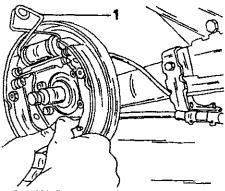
Вставить тормозные колодки сверху в колесный тормозной цилиндр и развести снизу, чтобы их можно было упереть в нижний упор. Пружинная скоба (1) препятствует выходу поршней.
